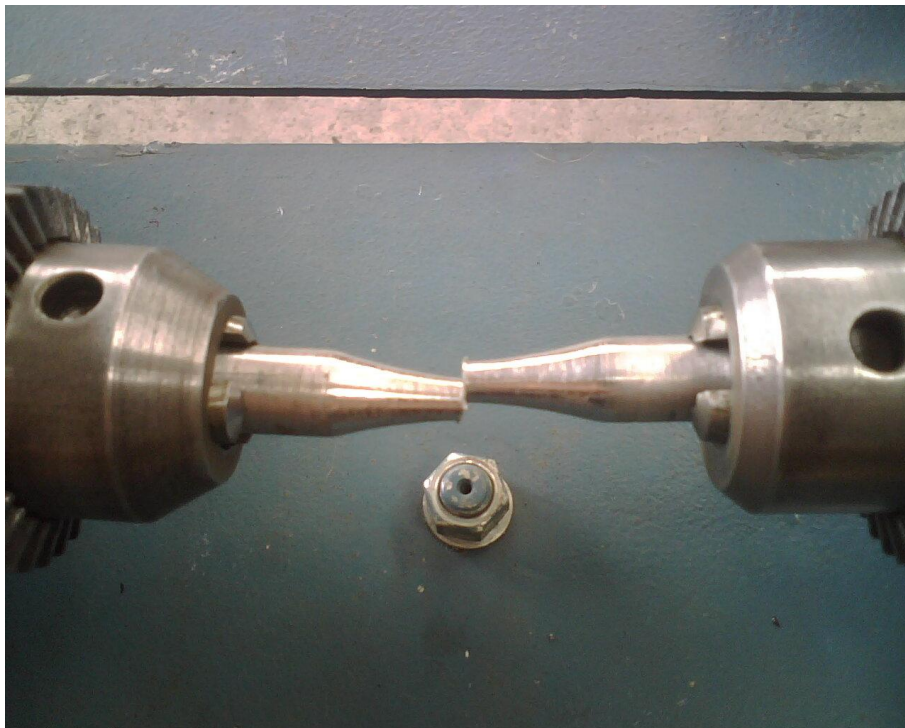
FOTOGRAFÍA DE UNA PROBETA FRACTURADA
